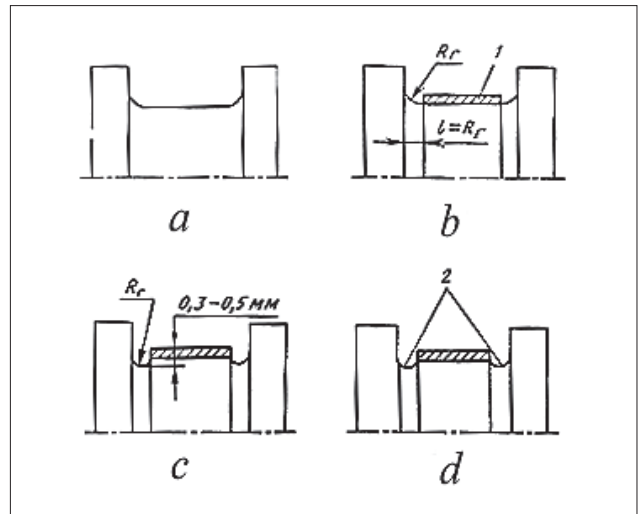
Шейка изношенного вала: а – наплавленная; б – с углубленными галтелями; 1 – наплавленный металл; с – упрочненная дробью; 2 – зона упрочнения дробью (d)
